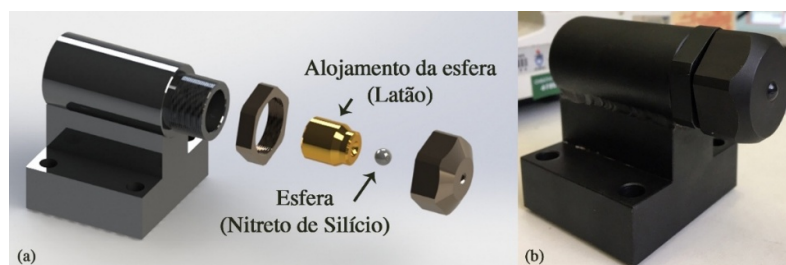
Suporte usado na fixação da esfera (a) em vista explodida e (b) montado com a esfera fixada.
